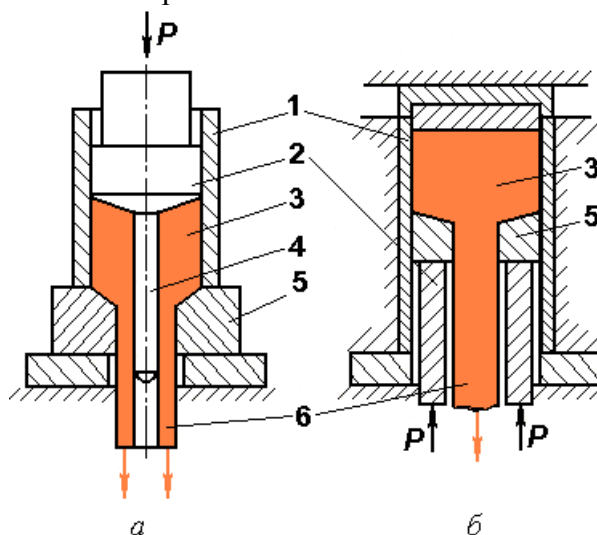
Прессование прямое (а) и обратное (б): 1 – контейнер; 2 – пуансон; 3 – заготовка; 4 – игла; 5 – матрица; 6 – профиль
